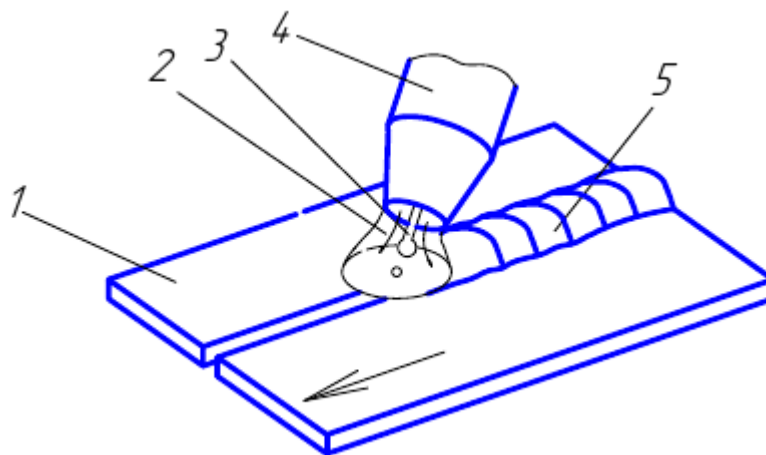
Схема сварки плавящимся электродом в защитных газах:
